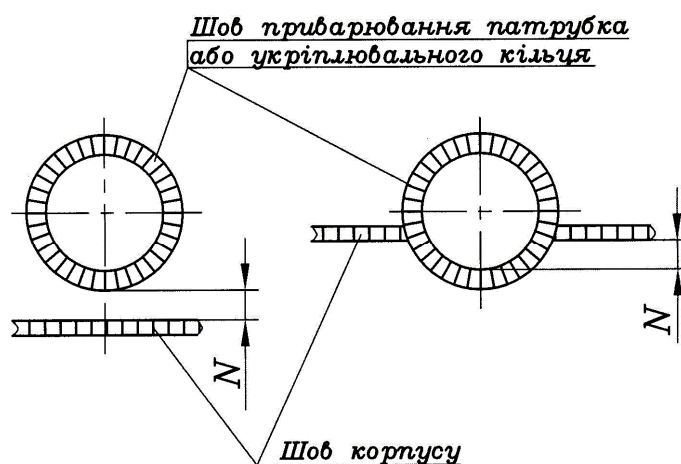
Схема визначення відстані між краєм шва корпусу і краєм приварювання деталі
